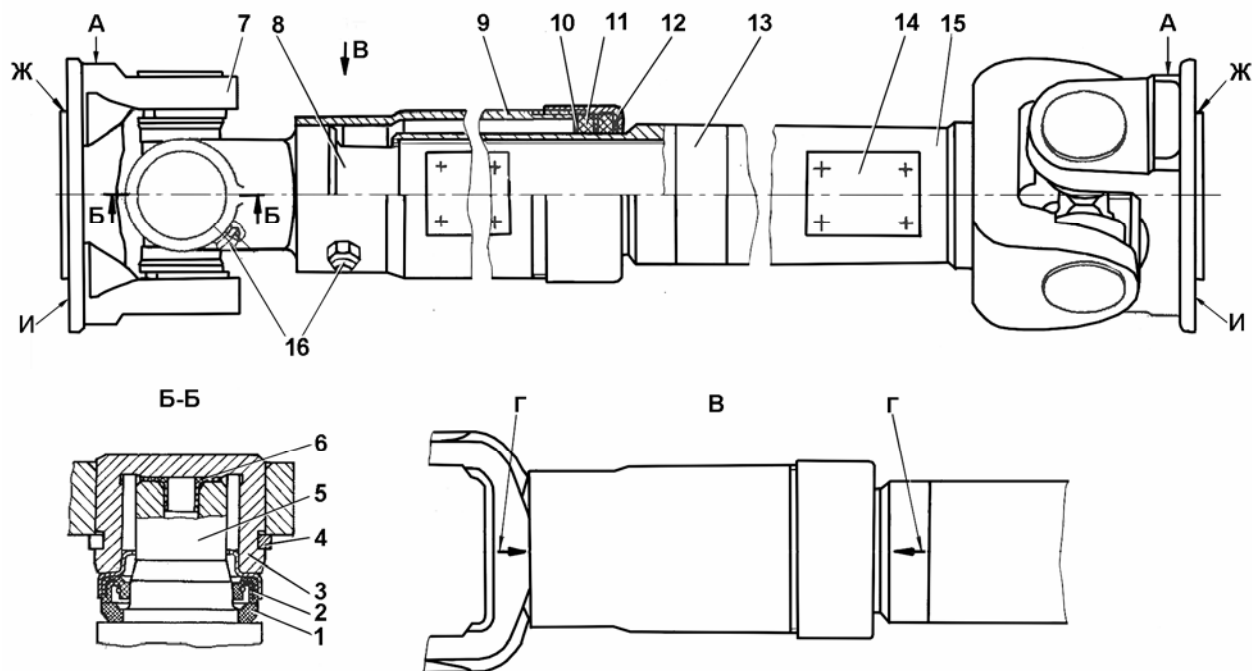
Карданный вал: А – места допустимых ударов при разборке; 1 – отражатель; 2 – манжета; 3 – игольчатый подшипник; 4 – стопорное кольцо; 5 – крестовина; 6 – торцовая шайба; 7 – фланец; 8 – шлицевая вилка; 9 – кожух; 10 – шайба; 11 – кольцо уплотнительное; 12 – обойма; 13 – шлицевая втулка; 14 – балансировочная пластина; 15 – труба; 16 – пресс-масленка с колпачком
